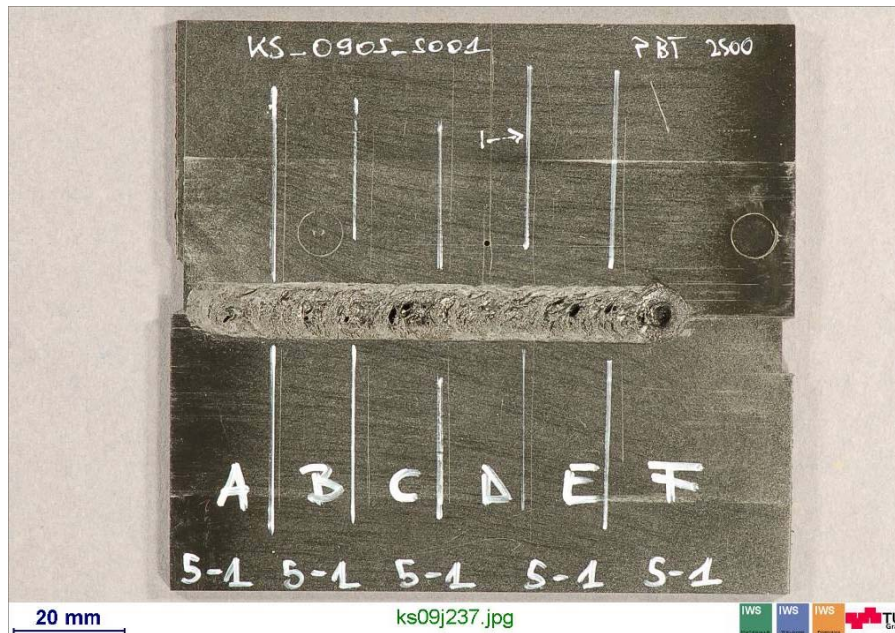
Herausnehmen der Proben aus den geschweißten Platten (B, C, E Zugproben; D Makro)
